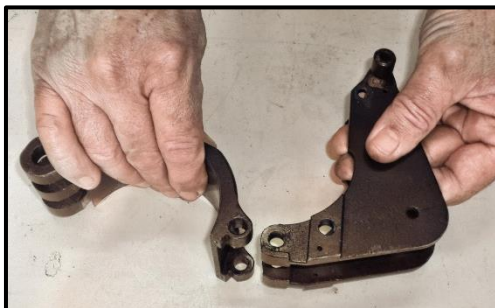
Separação da alavanca de travamento do corpo da braçadeira superior
